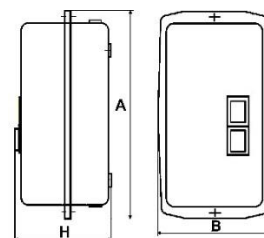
Контактор реверсивный ПМЛ-5560М
